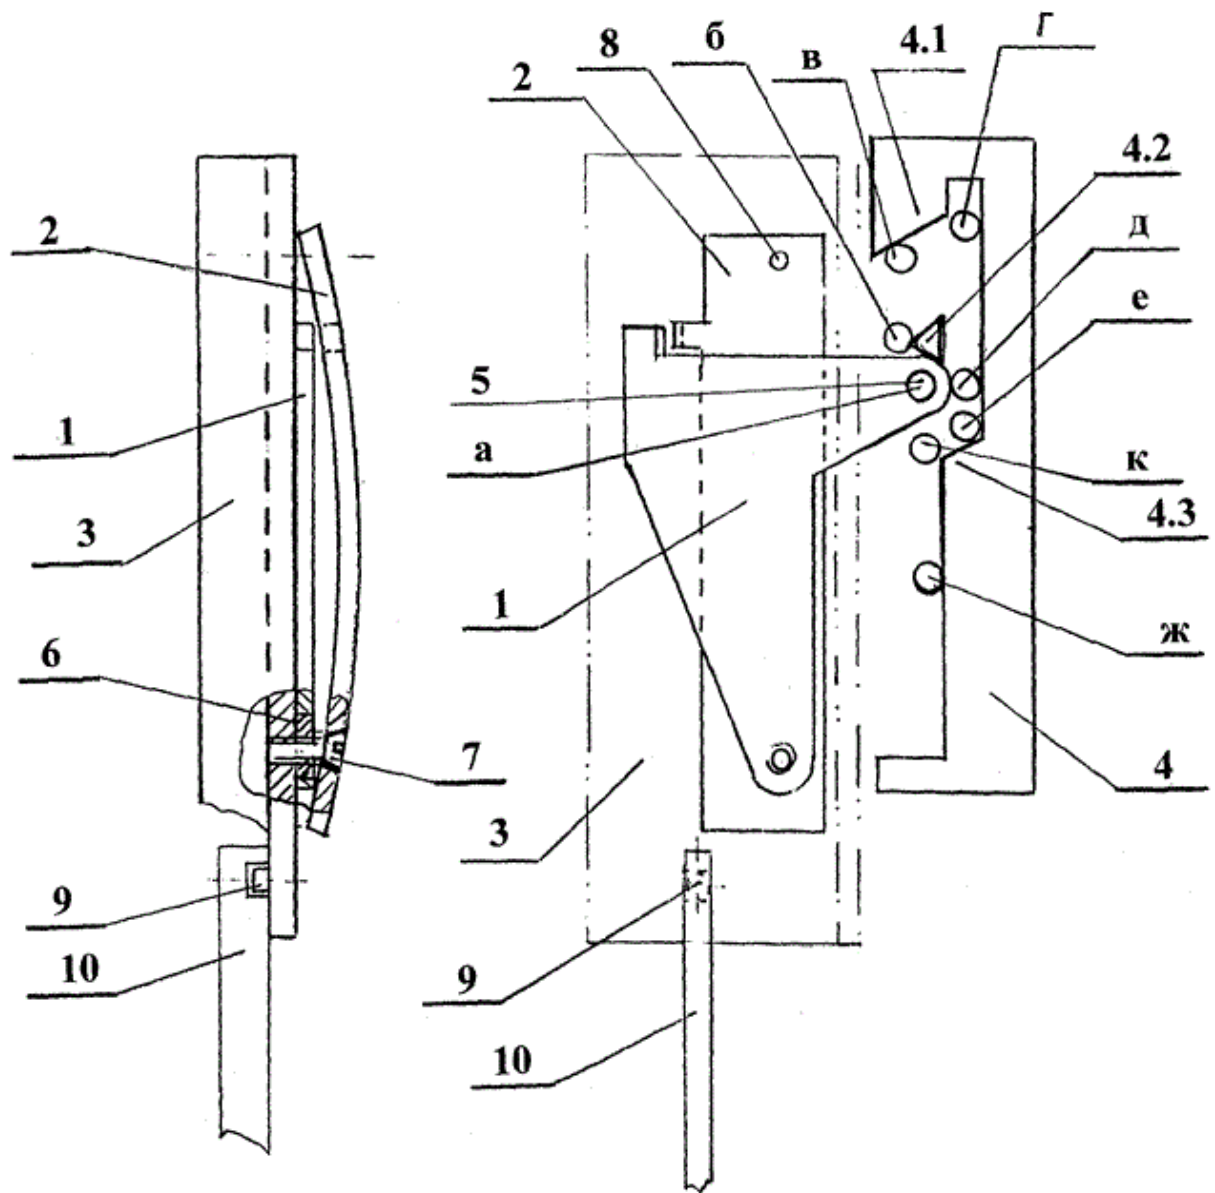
Пристрій для обрізки голкової нитки
